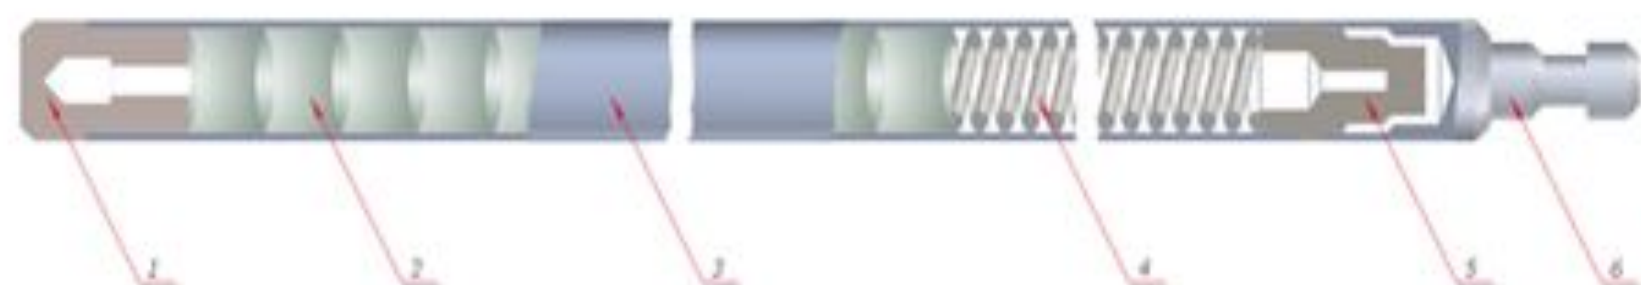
Устройство ТВЭЛА реактора РБМК: 1 — заглушка; 2 — таблетки диоксида урана; 3 — оболочка из циркония; 4 — пружина; 5 — втулка; 6 — наконечник. ¶
